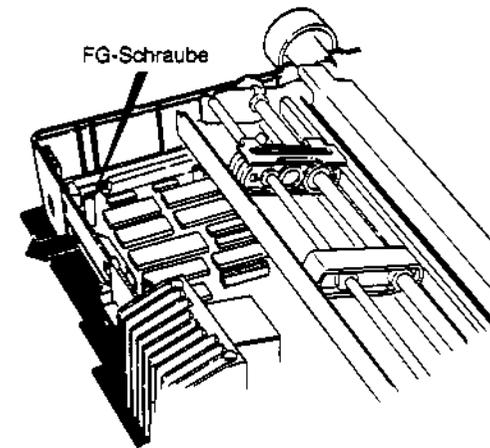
Lage der FG-Schraube für das Massekabel
